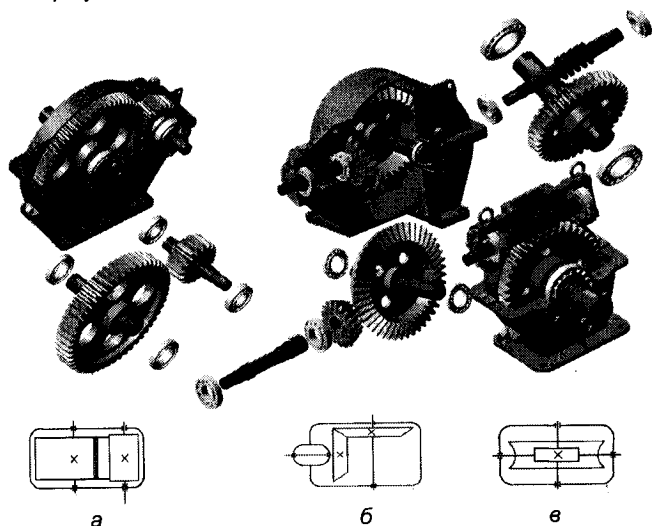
Редуктор: а – циліндричний, б – конічний, в – черв'ячний
